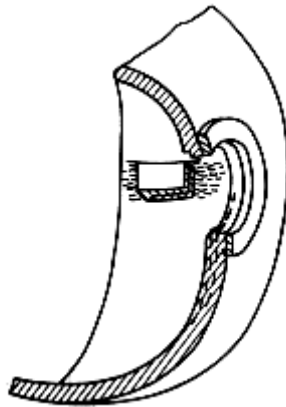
Схема расположения трещин около шва приварки лапы затвора лаза и у шва приварки усиления кромки лаза (здесь также показана схема выхода расслоений листа на кромку лазового отверстия)
